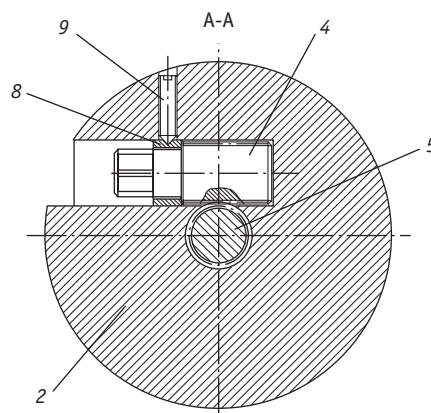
Сечение А-А устройства регулировки вылета расточного резца
